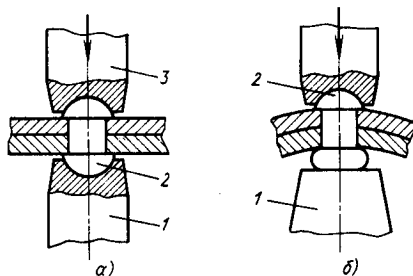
Схема клепки: а — обычным способом; б — обратным способом; 1 — поддержка; 2 — закладная головка заклепки; 3 — обжимка
